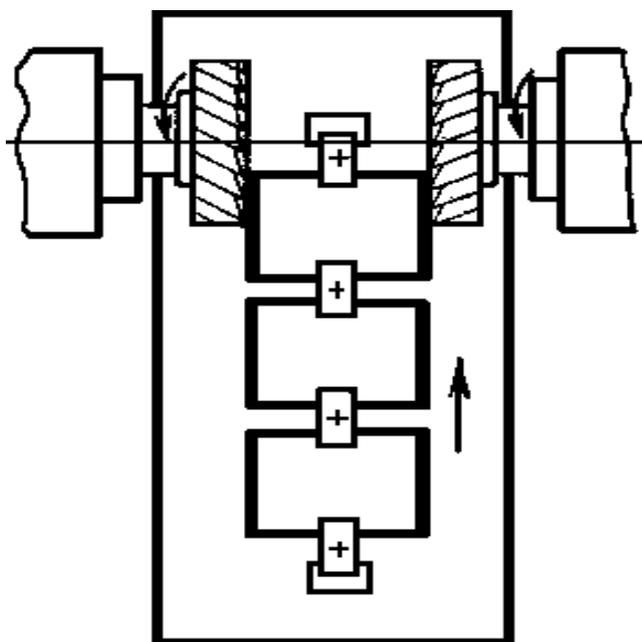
Обработка корпуса на продольно-фрезерном станке.
